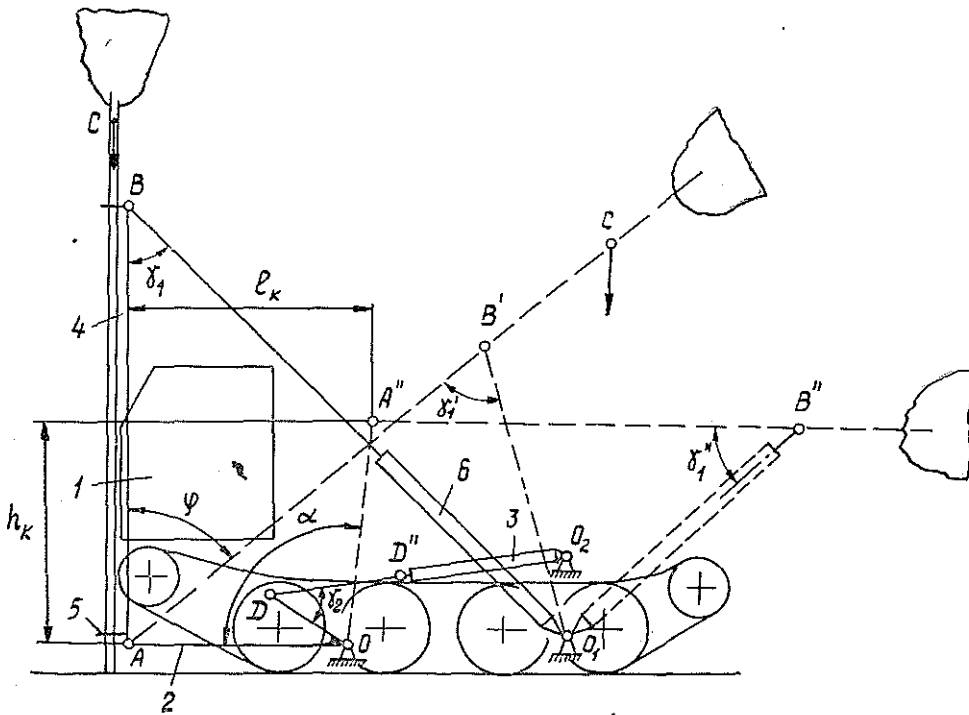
Кинематическая схема валочно-пакетирующего механизма на базе гусеничного трактора ТДТ-55.
